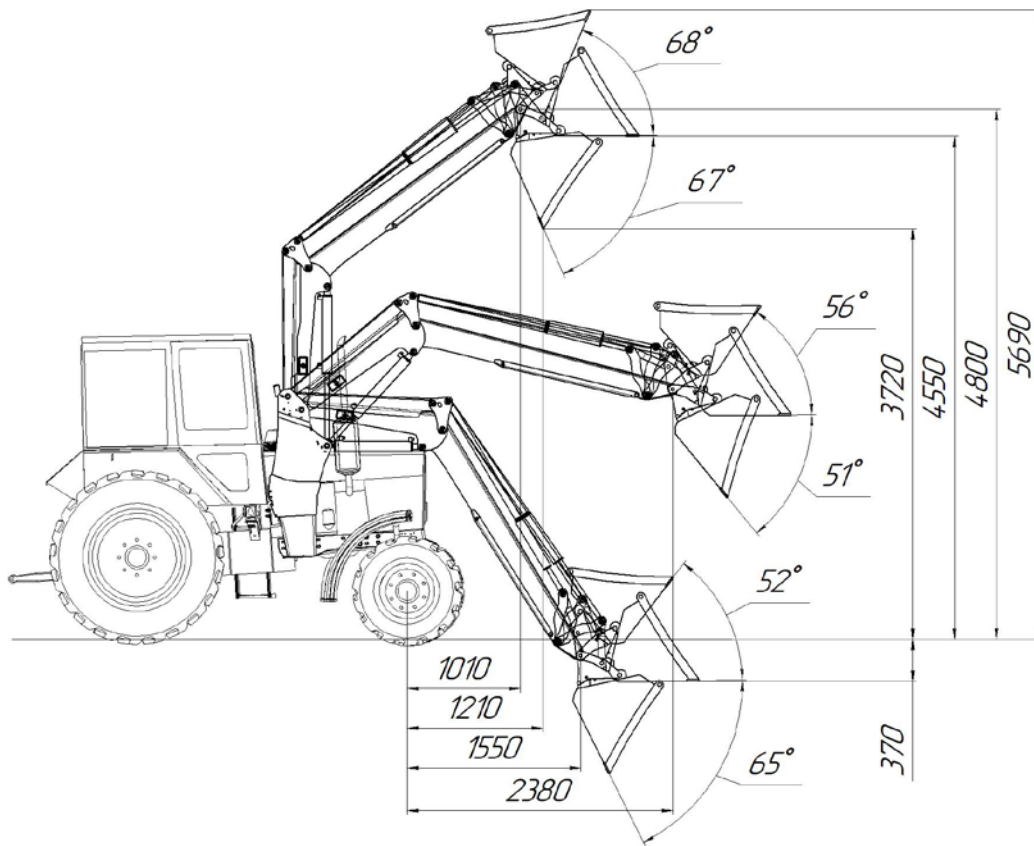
Габаритные размеры погрузчика Универсал 4.5
